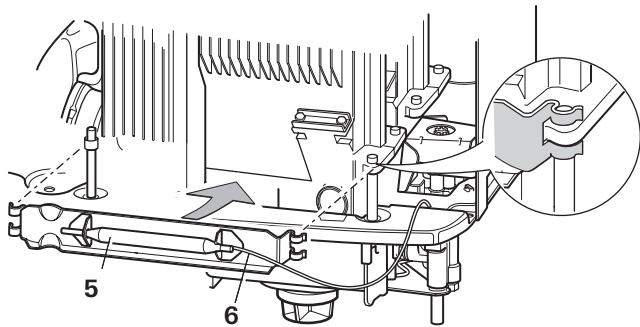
Fig. A (montaje a la derecha) / Fig. B (montaje a la izquierda)
